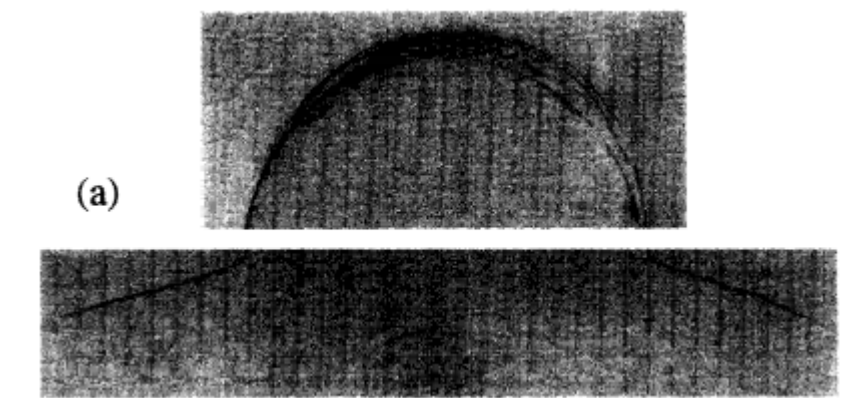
Ejemplo de fractura anillo, en la vista superior y fractura como en la vista frontal. [1]
